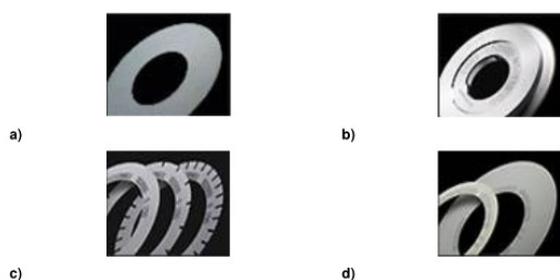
Discos de corte: a) disco de diamante e resina, b) disco tipo *hub*, c) disco serrilhado de diamante e resina e d) disco de metal.
